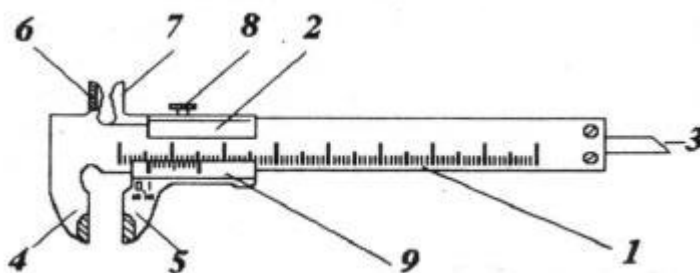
Устройство штангенциркуля ШЦ-1
